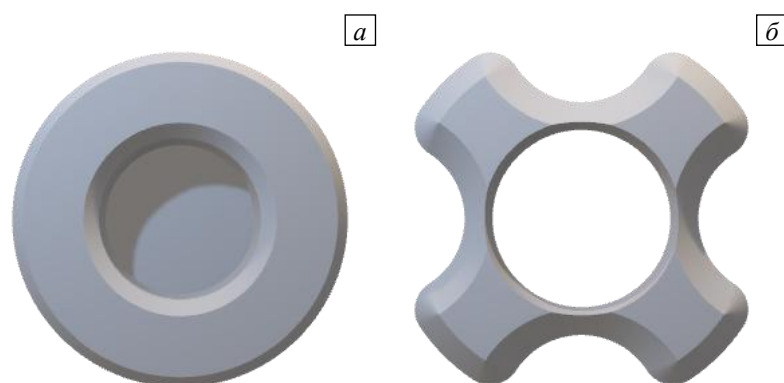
Форма поддона (а) и направляющей (б) для образца
